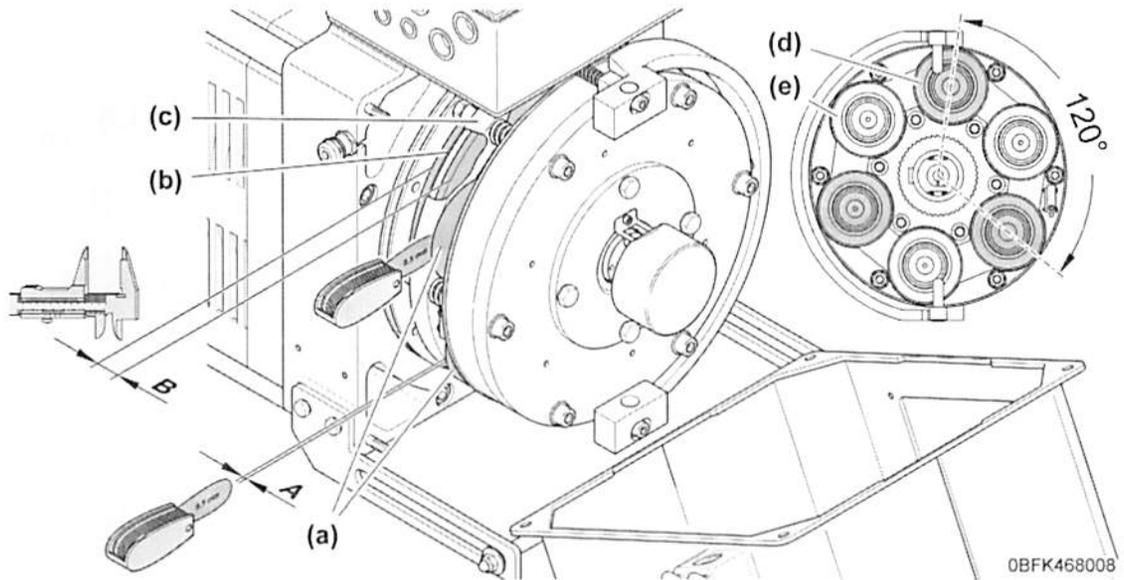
Luftspalt und Bremsscheibe prüfen
